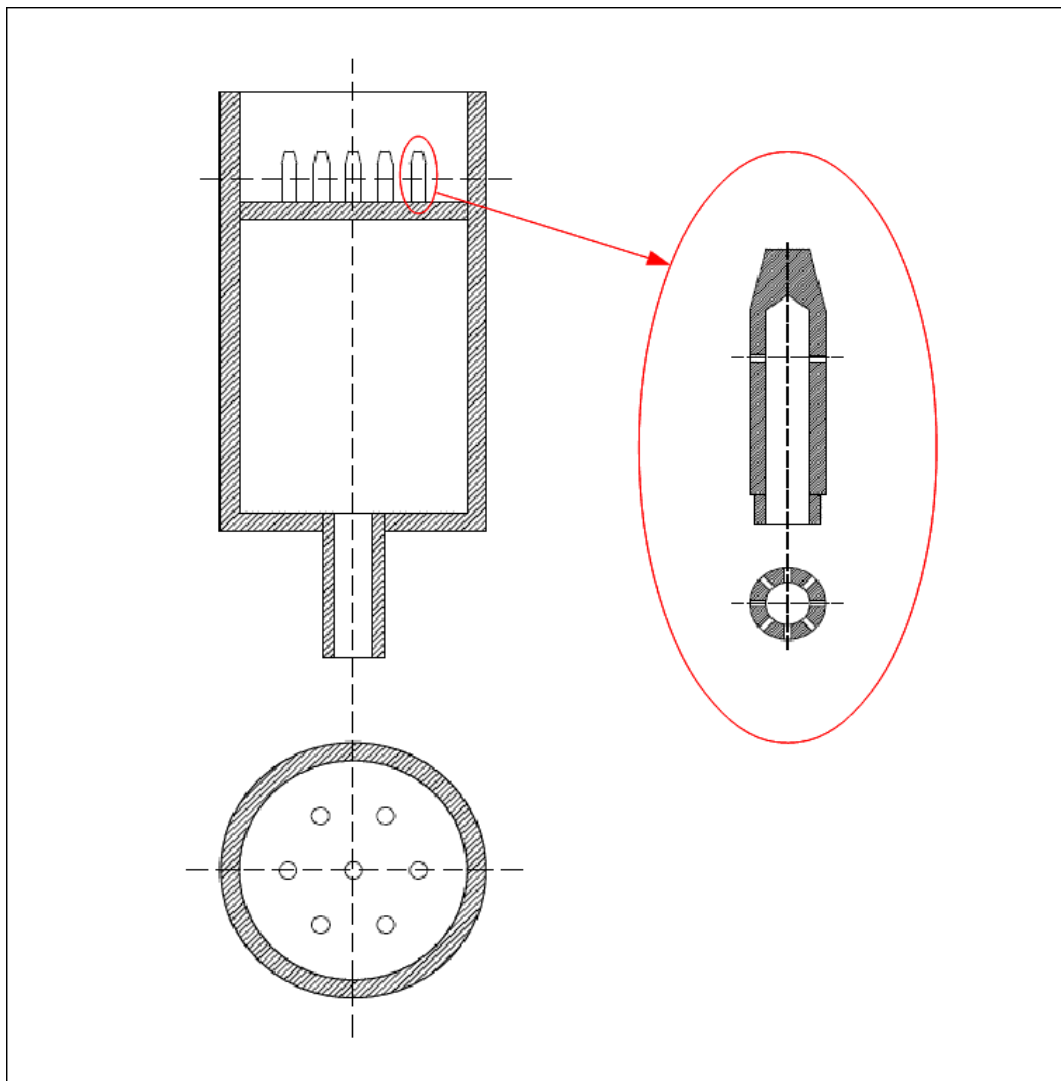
Plano: Plénium-distribuidor-lecho y detalle de los tuyeres.-
